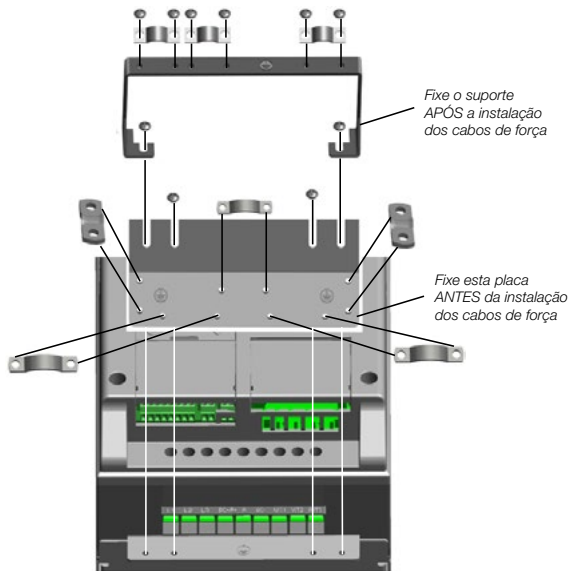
Monte a placa PE e suporte a cabo API, MI4 - MI5
